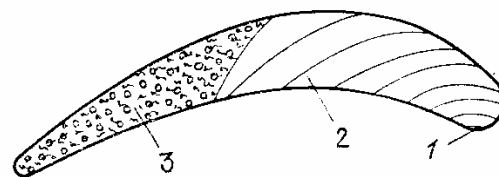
Усталостный излом лопатки: 1 — место зарождения трещины; 2 — зона развития трещины; 3 — зона окончательного излома
